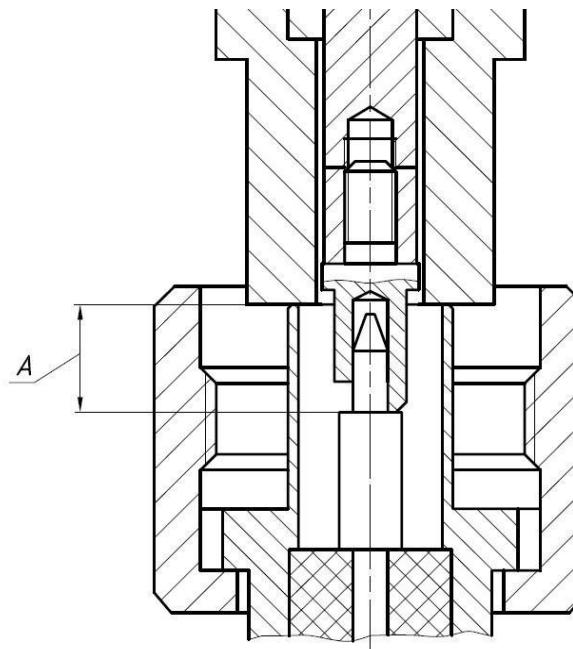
Проверка размера «A» соединителя «вилка»
